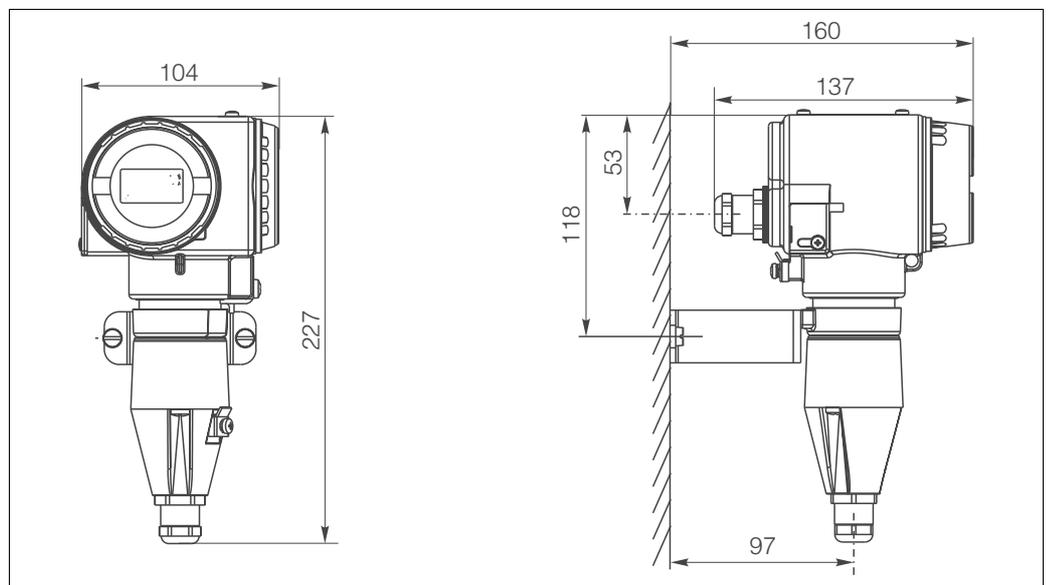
MyPro für Wandmontage mit Befestigungsbügel (bei CXM431-xxx2xx im Lieferumfang)
